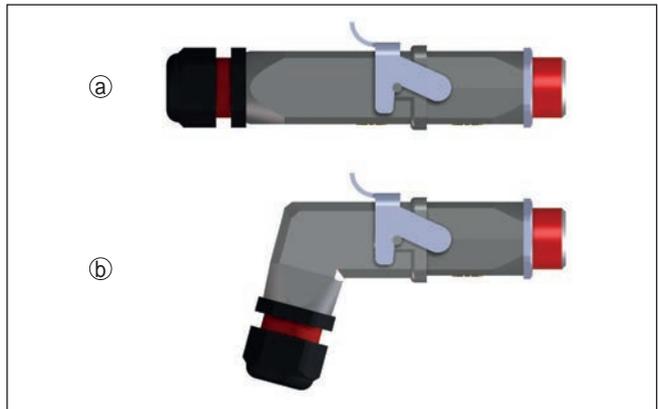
Steckverbinder Harting HAN 8D - gerade und abgewinkelte Ausführung
